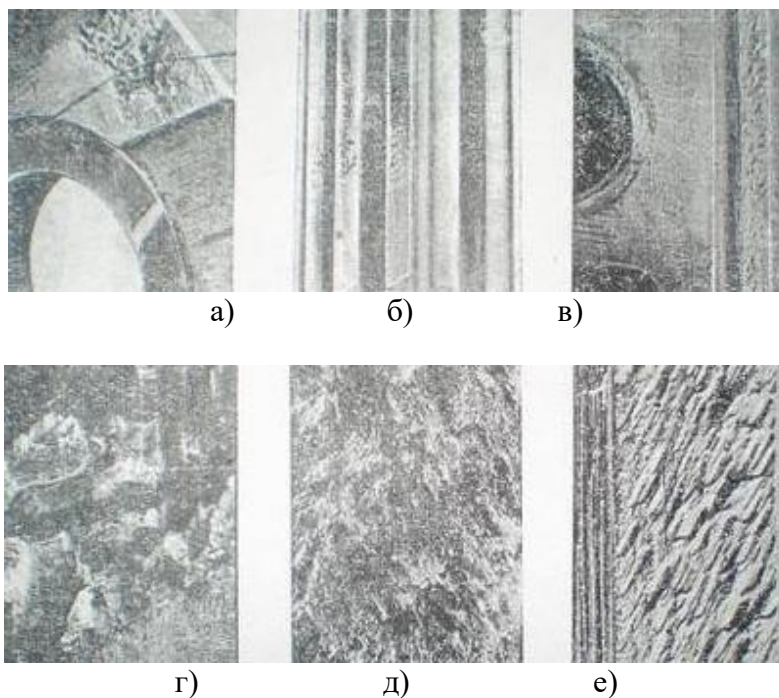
Ділянки поверхонь деталей, що пошкоджені фретинг-корозією:
